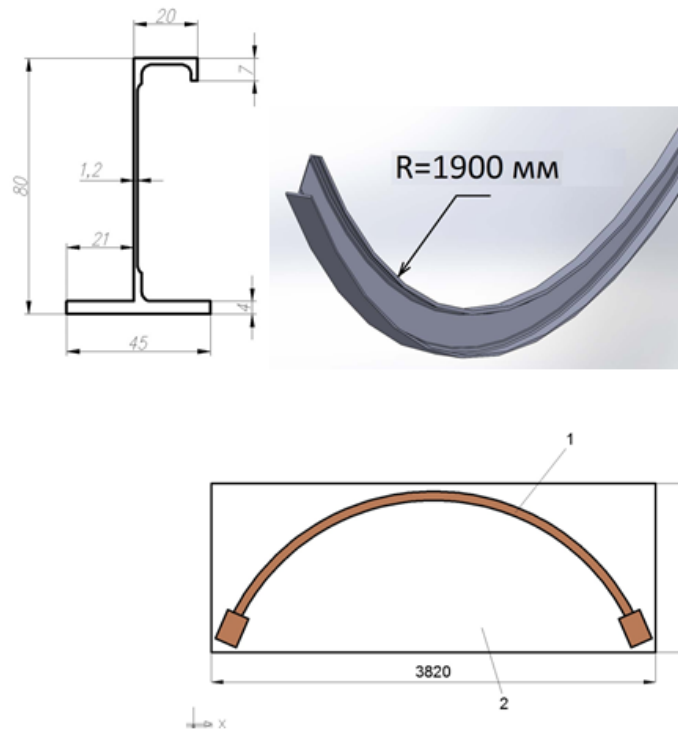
Параметры заготовки шпангоута, получаемой фрезерной обработкой на станке с ЧПУ
